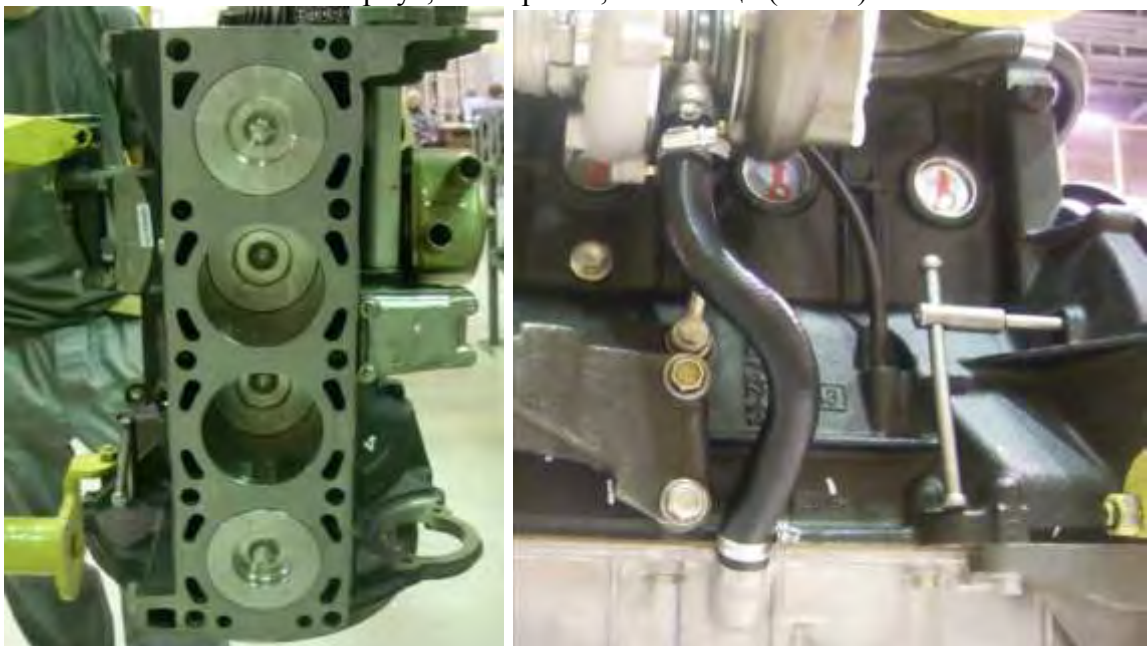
ЗМ 7820-4582 Штифт установочный коленчатого вала:
